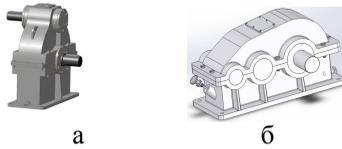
Вертикальный одноступенчатый (а) и горизонтальный двухступенчатый (б) цилиндрические редукторы
